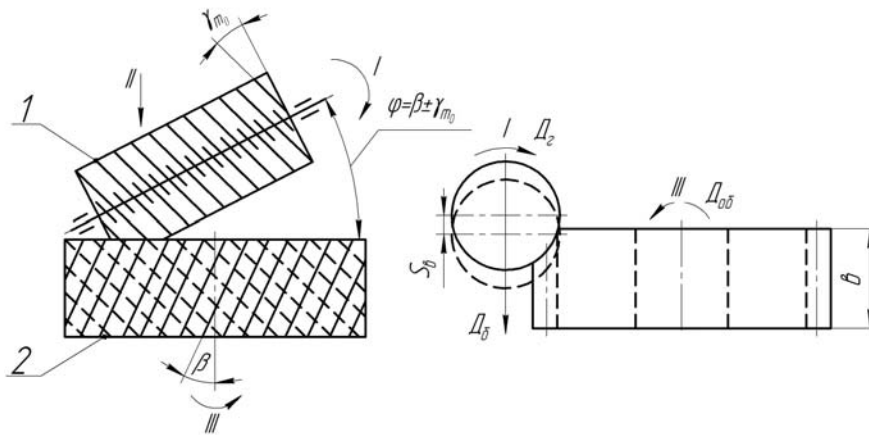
Схема установки фрезы относительно заготовки и основные движения при нарезании косозубого колеса
